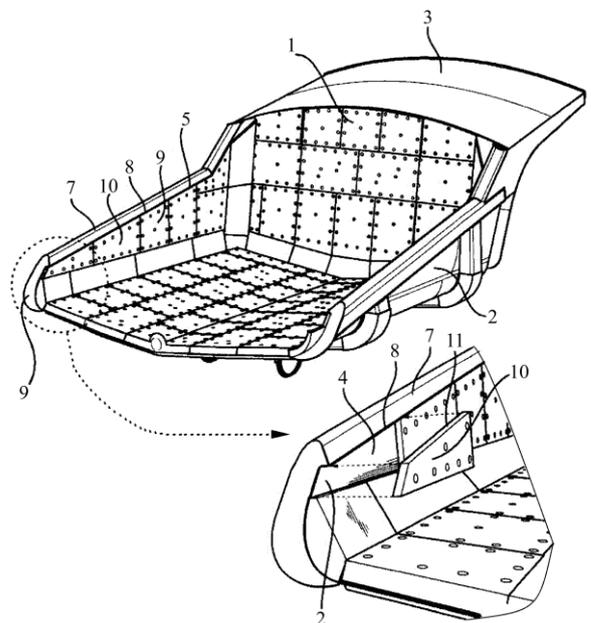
Кузов карьерного самосвала и способ его изготовления (RU2758171C2)
